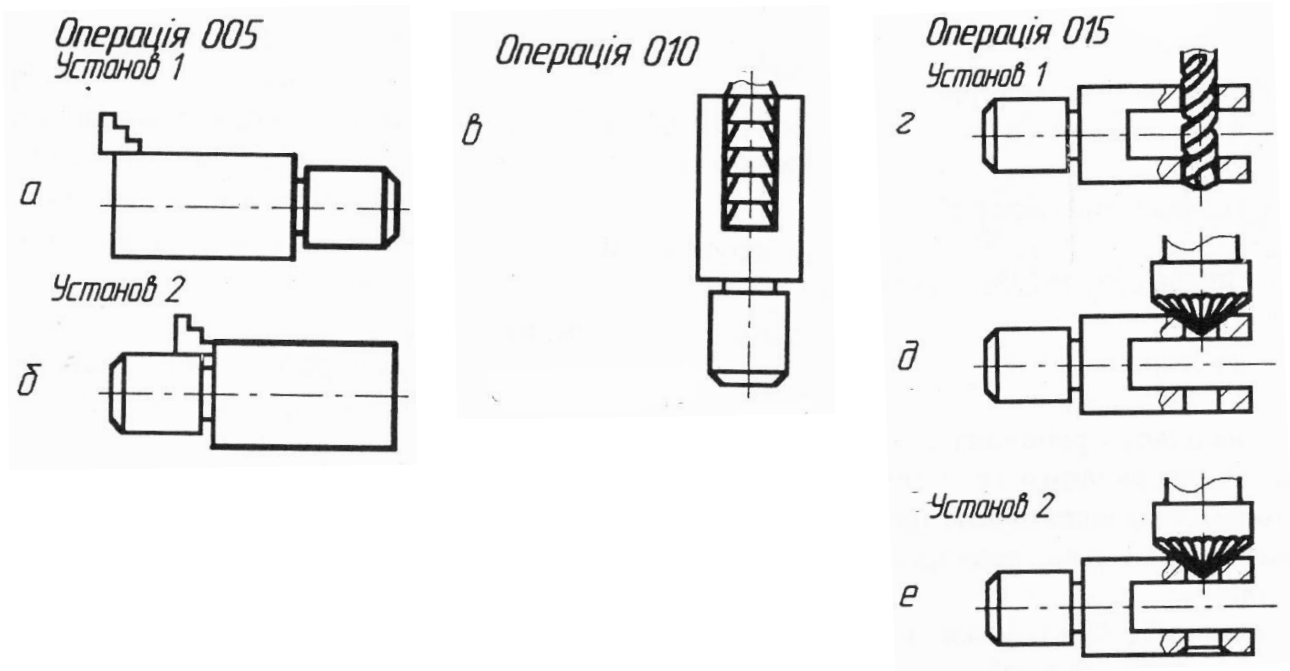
Схема технологічного процесу обробки вилки карданного валу
